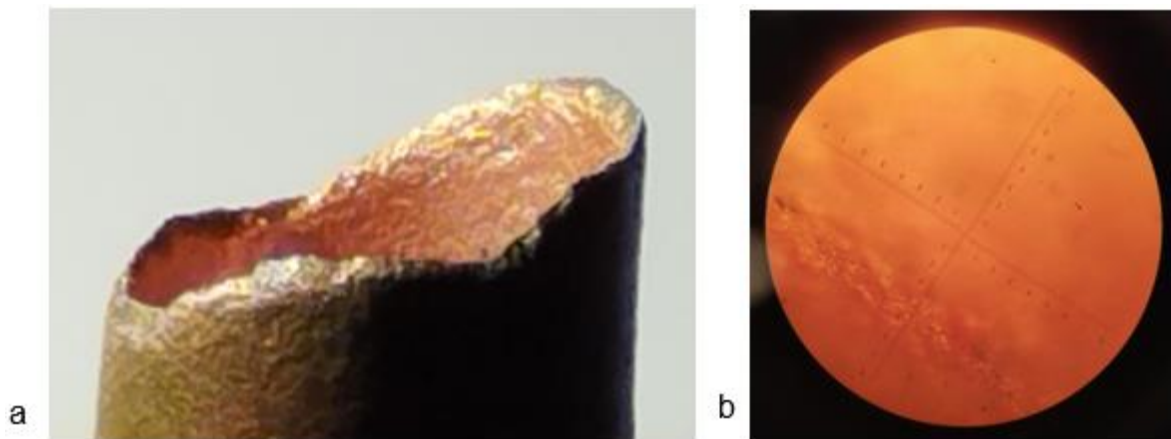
a) Fractura de la probeta. b) vista microscópica del borde de la probeta donde se presentó la fractura.
